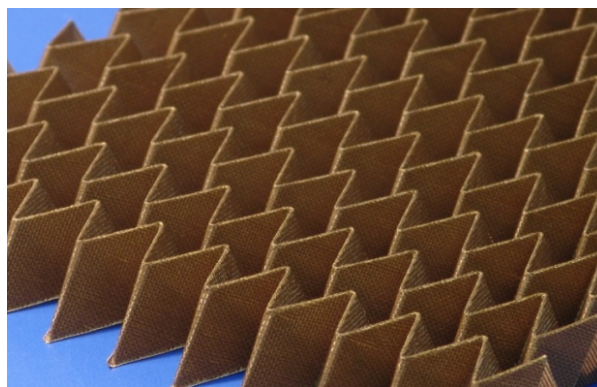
Образец наполнителя типа z-гофр из органопластика
